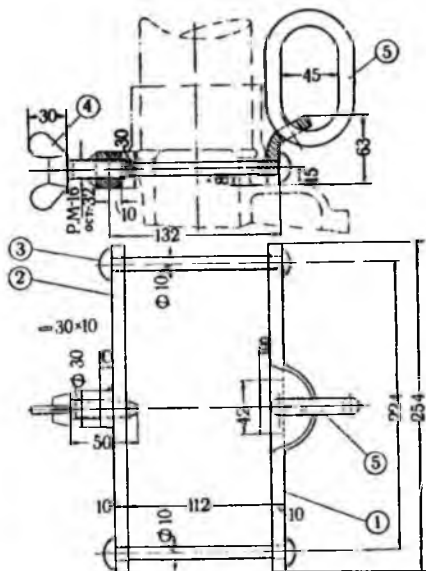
Схватка для всасывающего и выхлопного коллектора трактора СХТЗ-НАТИ:
